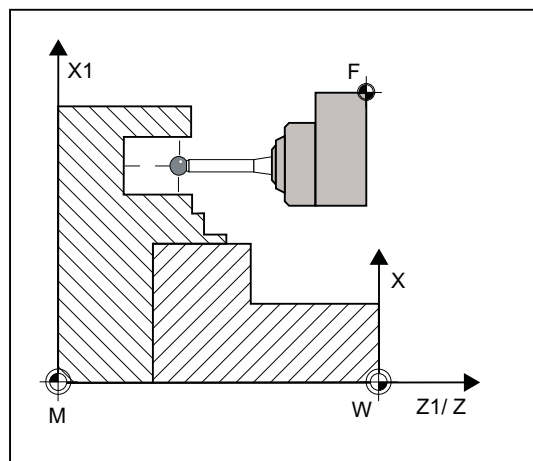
Калибровка измерительного щупа детали, пример: Калибровка в референтном пазу
